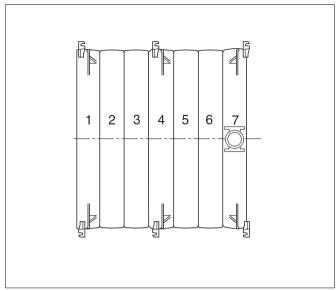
Draufsicht: Kesselblock (7 Kesselglieder) mit Konsolen
